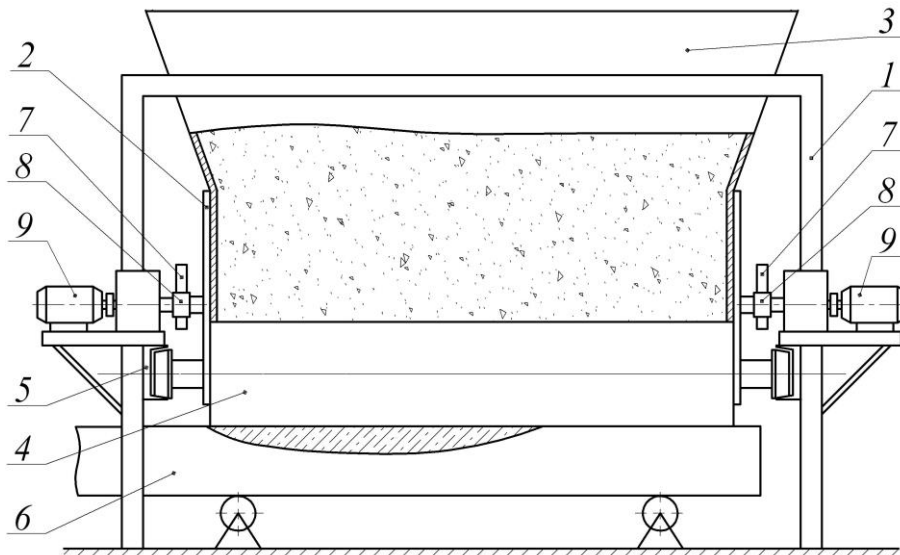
Роликова формувальна установка з кулачковим приводним механізмом
